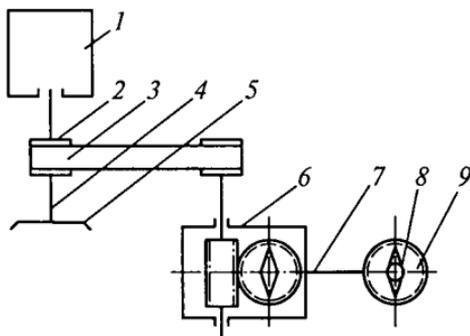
Кинематическая схема привода колес и рабочего органа газонокосилки:
